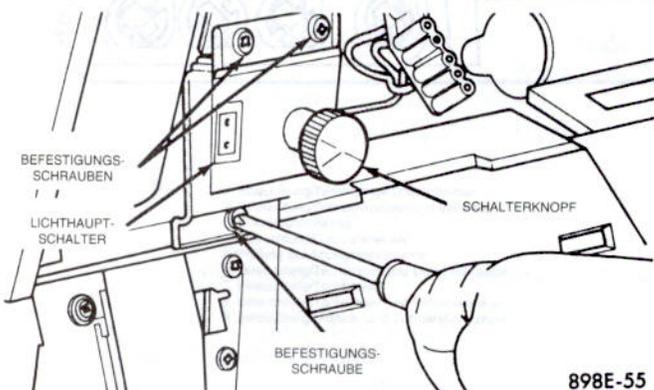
Befestigungsschrauben des Lichthauptschalters
